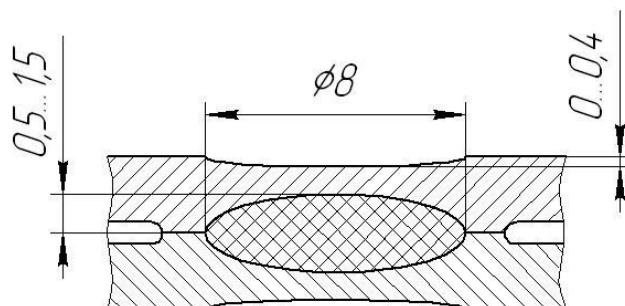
Геометрические размеры сварной точки по ГОСТ 15878-79 для деталей 2+2 мм
